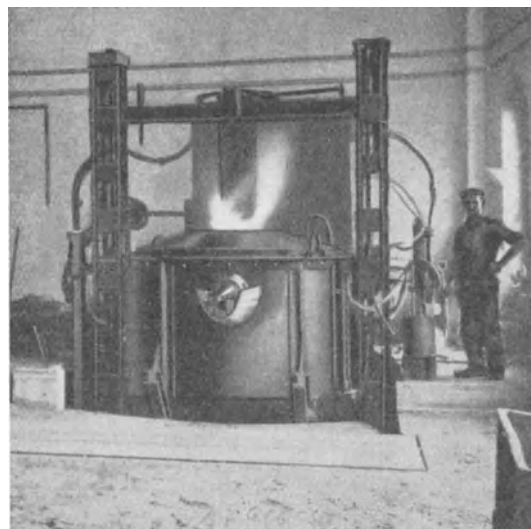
Girodofen für 3-t-Einsatz, Ansicht.
